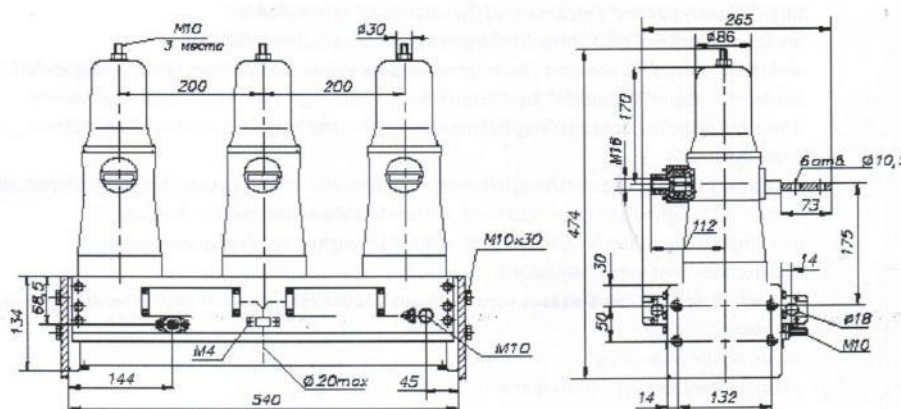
Габаритные и установочные размеры выключателя ВВ/TEL-10-12,5.
